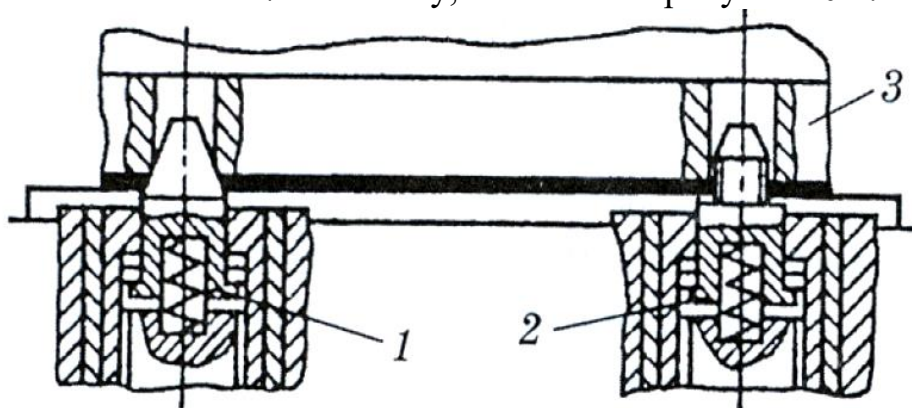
Схема установки корпусной детали: 1 – подпружиненный цилиндрический палец; 2 – ромбический палец; 3 – деталь
